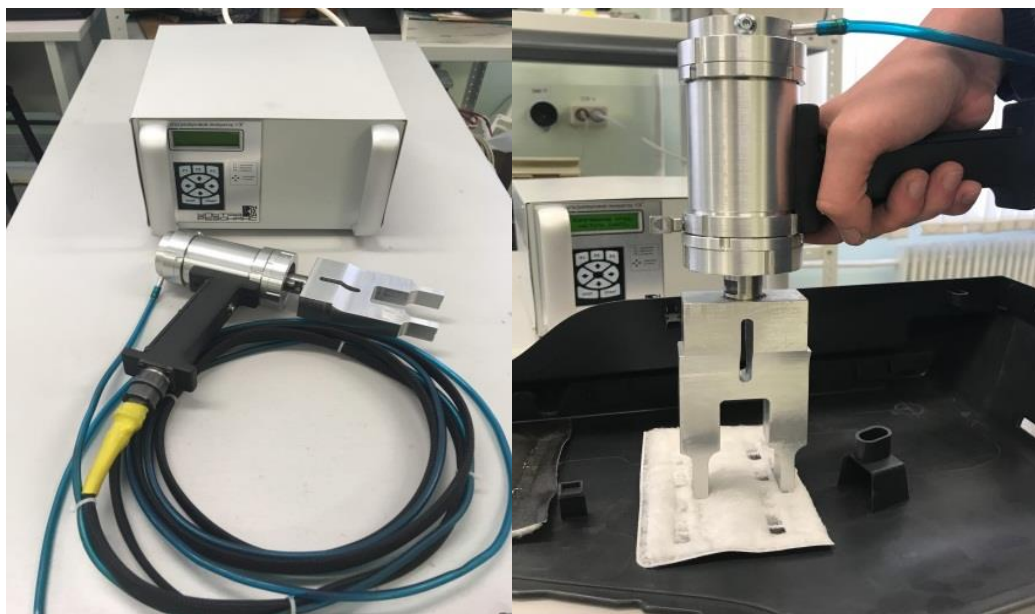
Процесс ультразвуковой сварки
